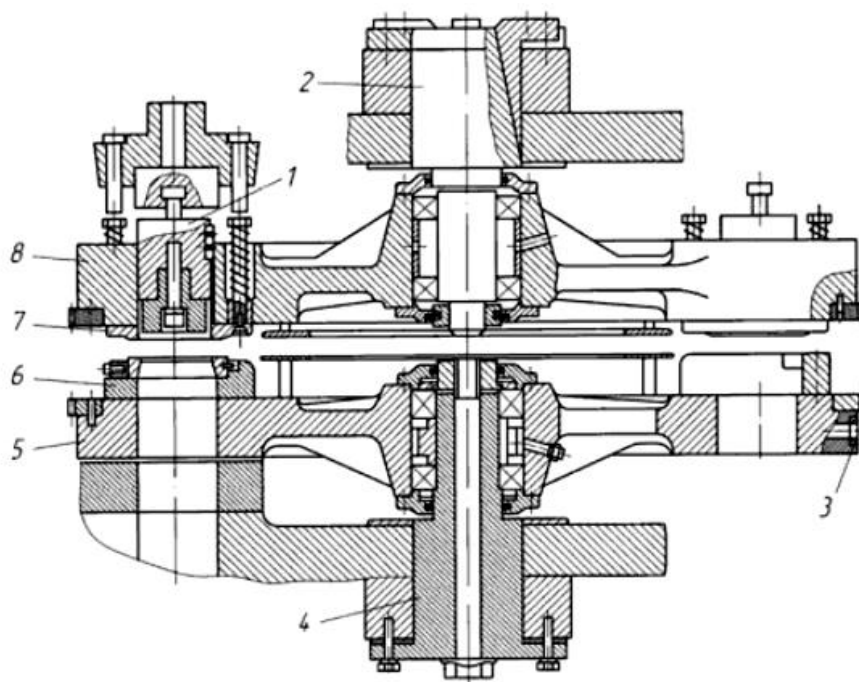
Конструктивна схема револьверної головки КПП: 1 – пуансонотримач, 2, 4 – вісь, 3 – конічна втулка, 6 – тримач матриць, 7 – притиск, 8 – верхній диск
